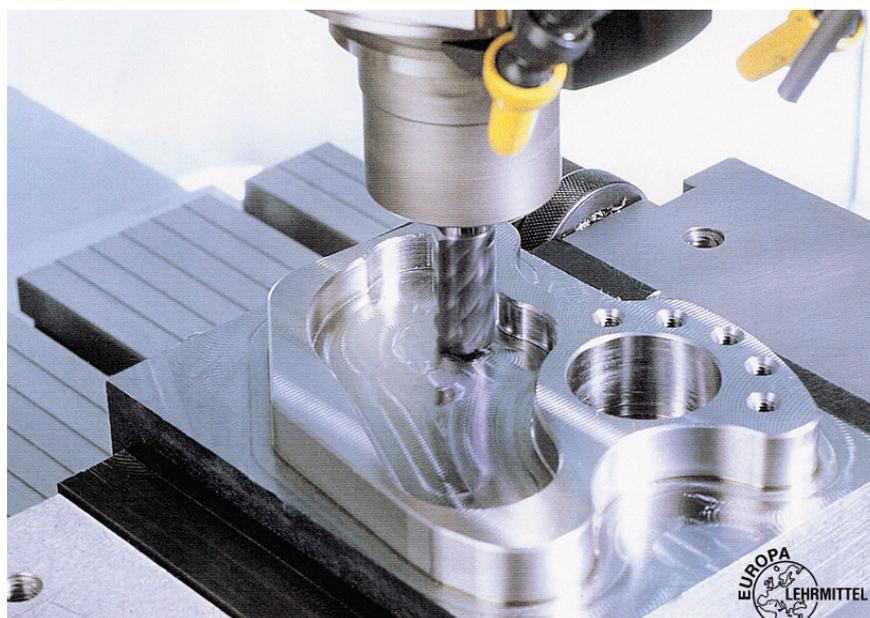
Фрезерование концевой фрезой по контуру
